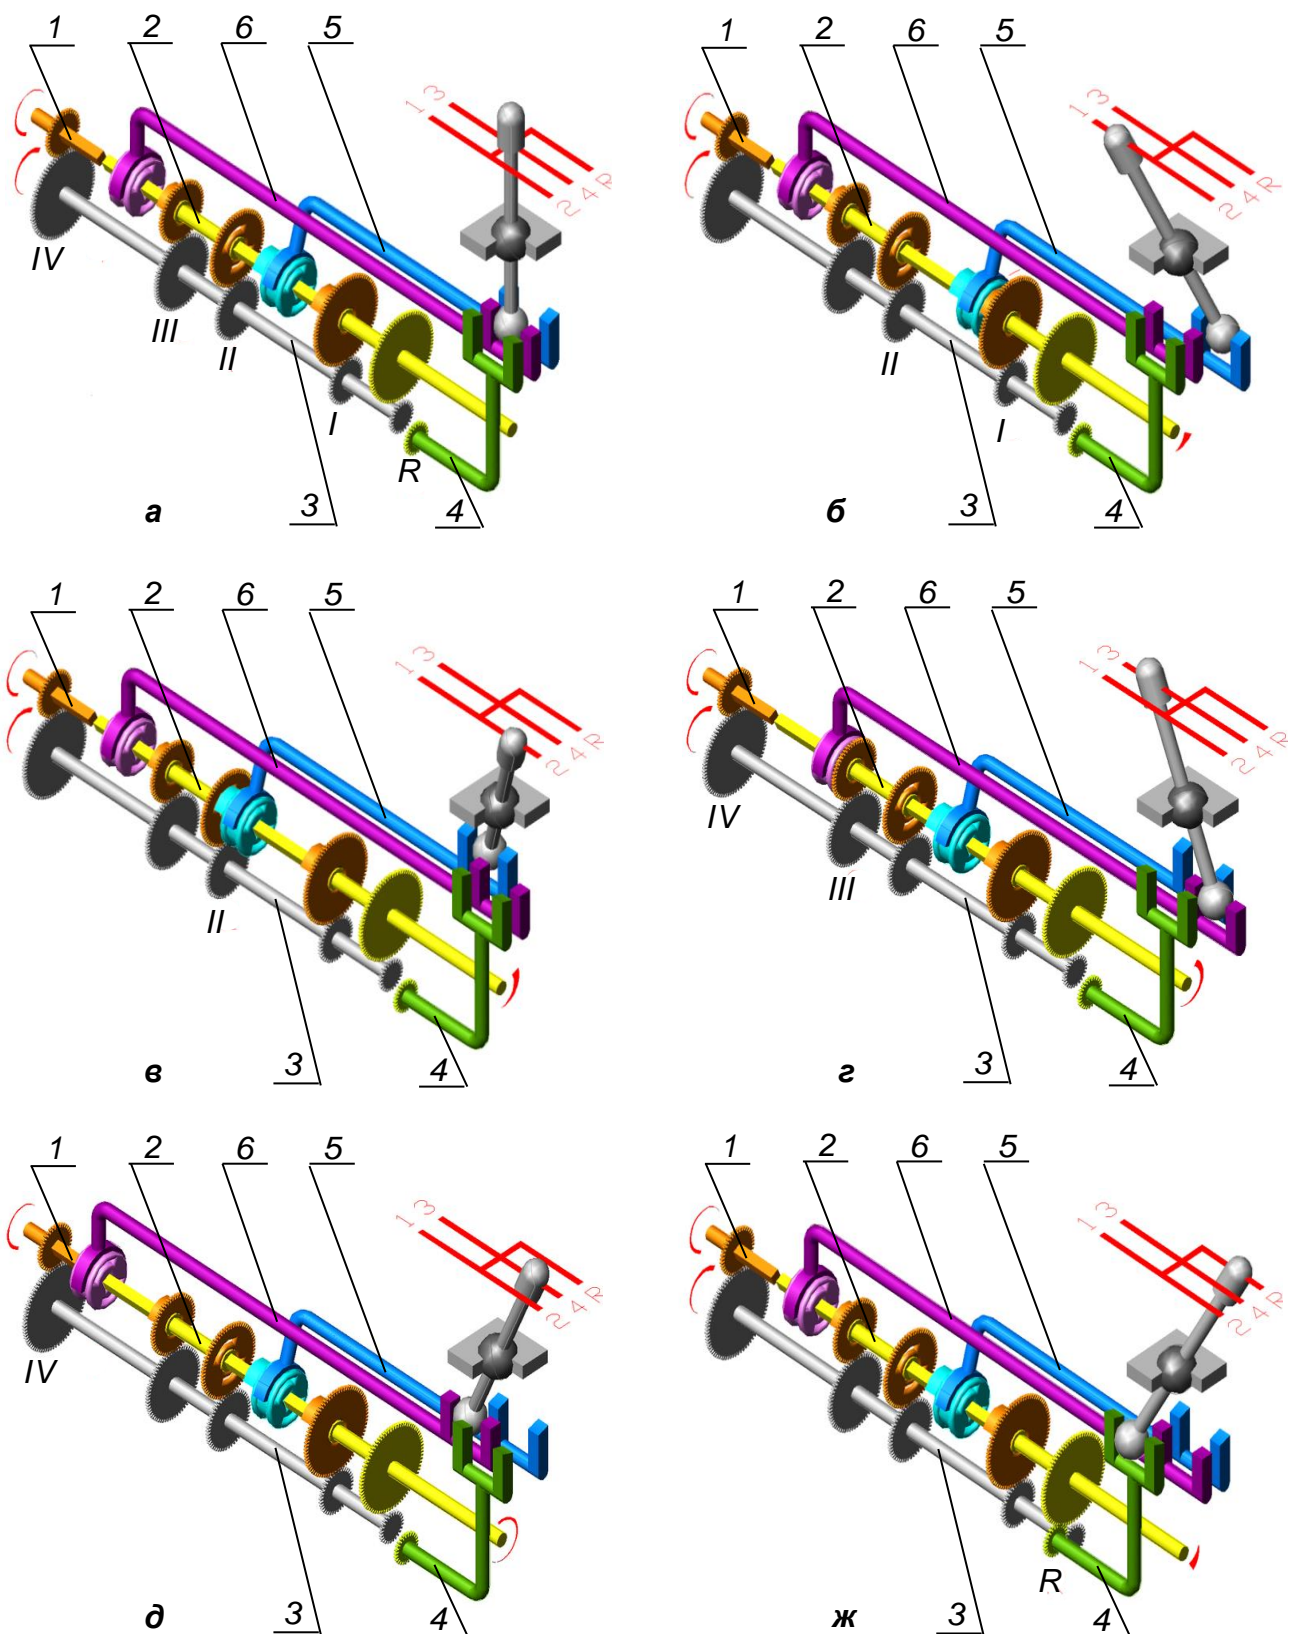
Принцип роботи синхронізатора коробки передач:
